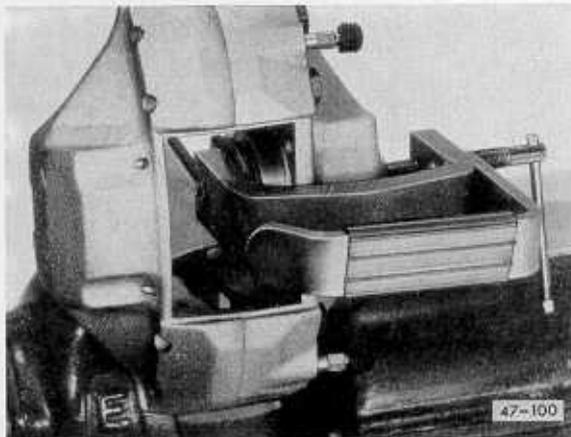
Kolben mit Kolbenmontagebügel eindrücken.
